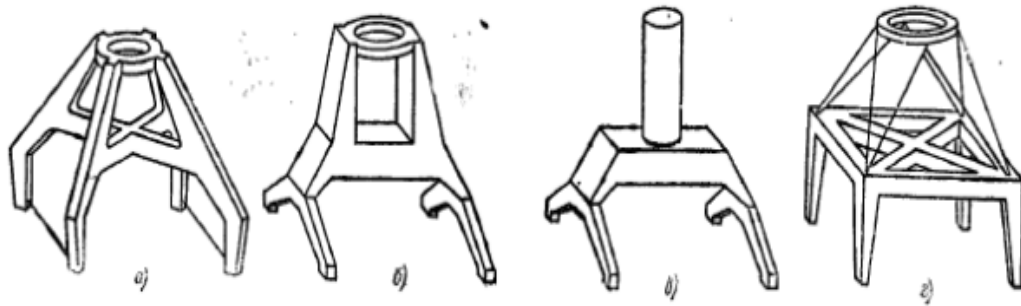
Портали: а - рамний чотирьохстійковий; би - рамний двостійковий; у - рамна вежа; г - рамний розкіс
